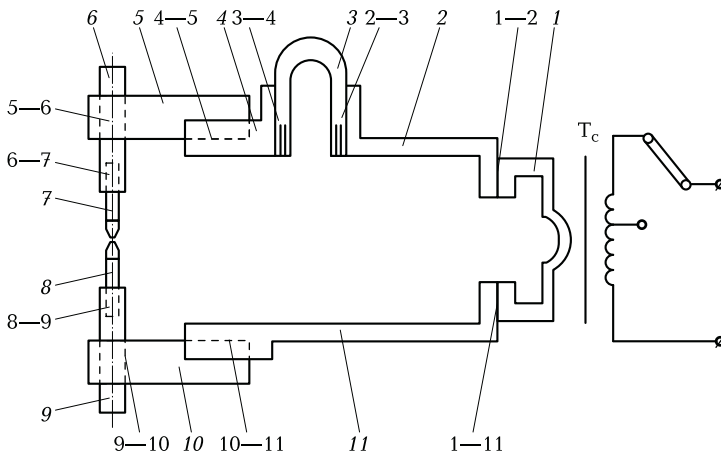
Схема вторичного контура машины для контактной точечной сварки:
